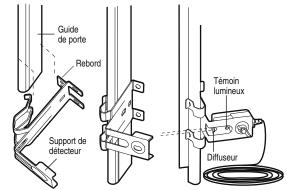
MONTAGE MURAL (CÔTÉ DROIT)
